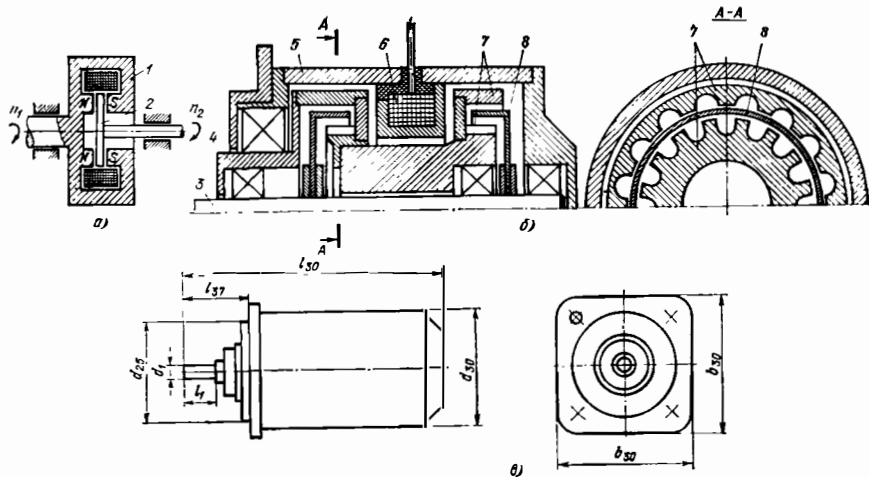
Конструктивная схема ГЭММ (а), бесконтактная ГЭММ серии МГБ (б) и ее основные размеры (в): 1 — индуктор (ведущая часть); 2 — диск из гистерезисного материала (ведомая часть); 3 — ведомый вал; 4 — ведущий вал; 5 — корпус; 6 — катушка; 7 — индуктор; 8 — стакан
